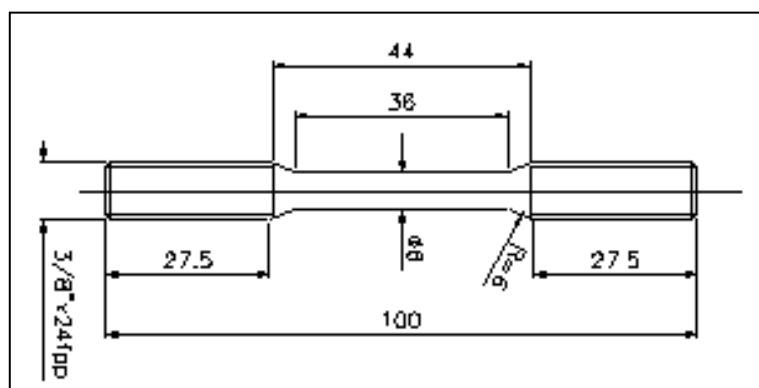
Dimensões do corpo de prova para ensaio de tração.
